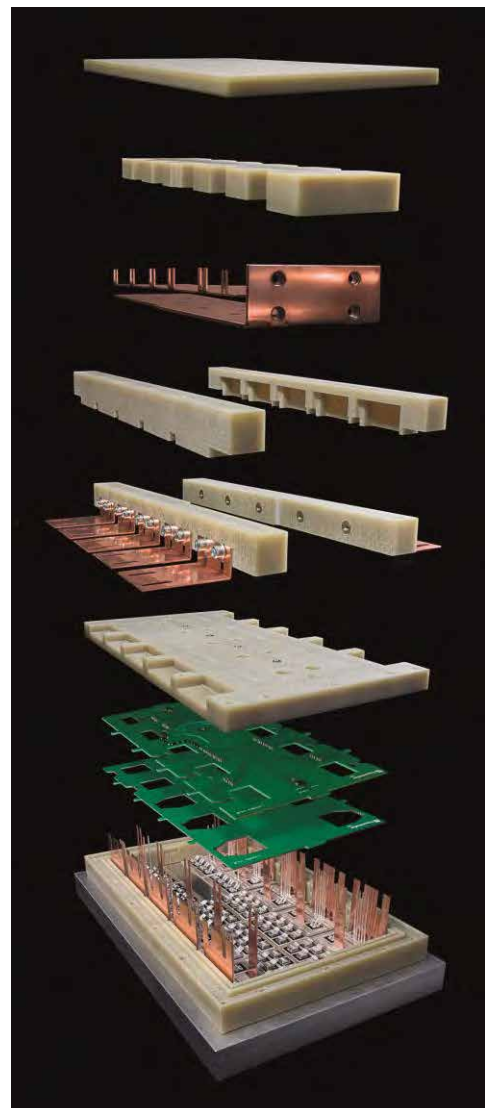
Explosionsdarstellung Schaltzellenprototyp
